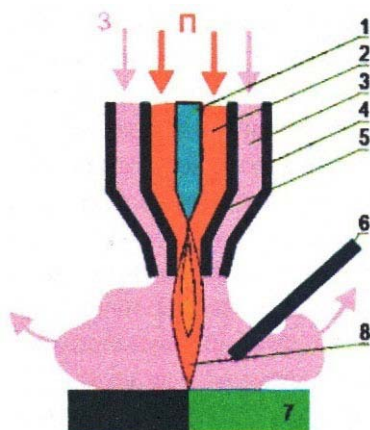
Схема плазменной сварки неплавящимся электродом с боковой подачей присадочной проволоки:
